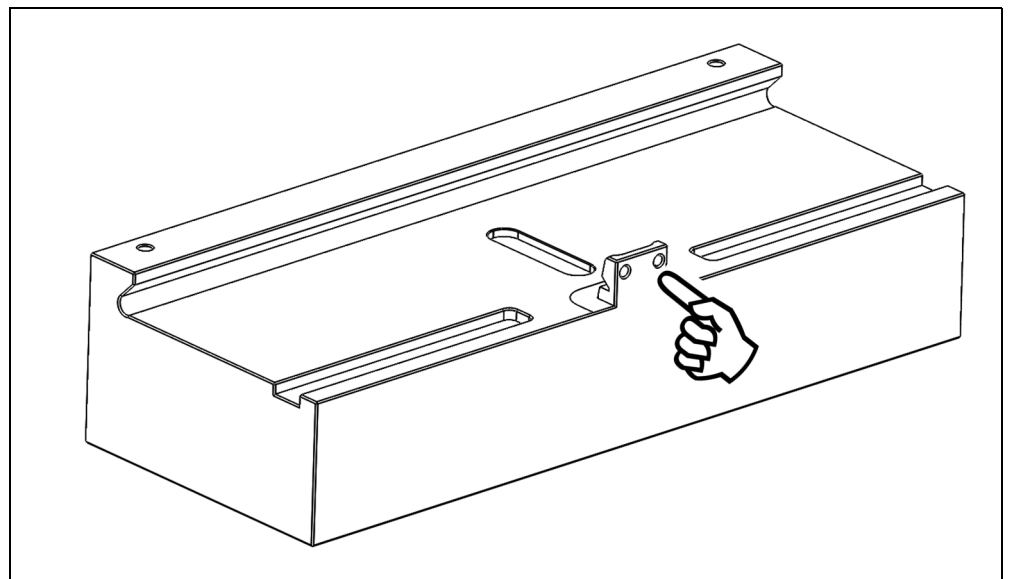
Hinweis auf die Gewinde für die Sicherheitsschrauben
